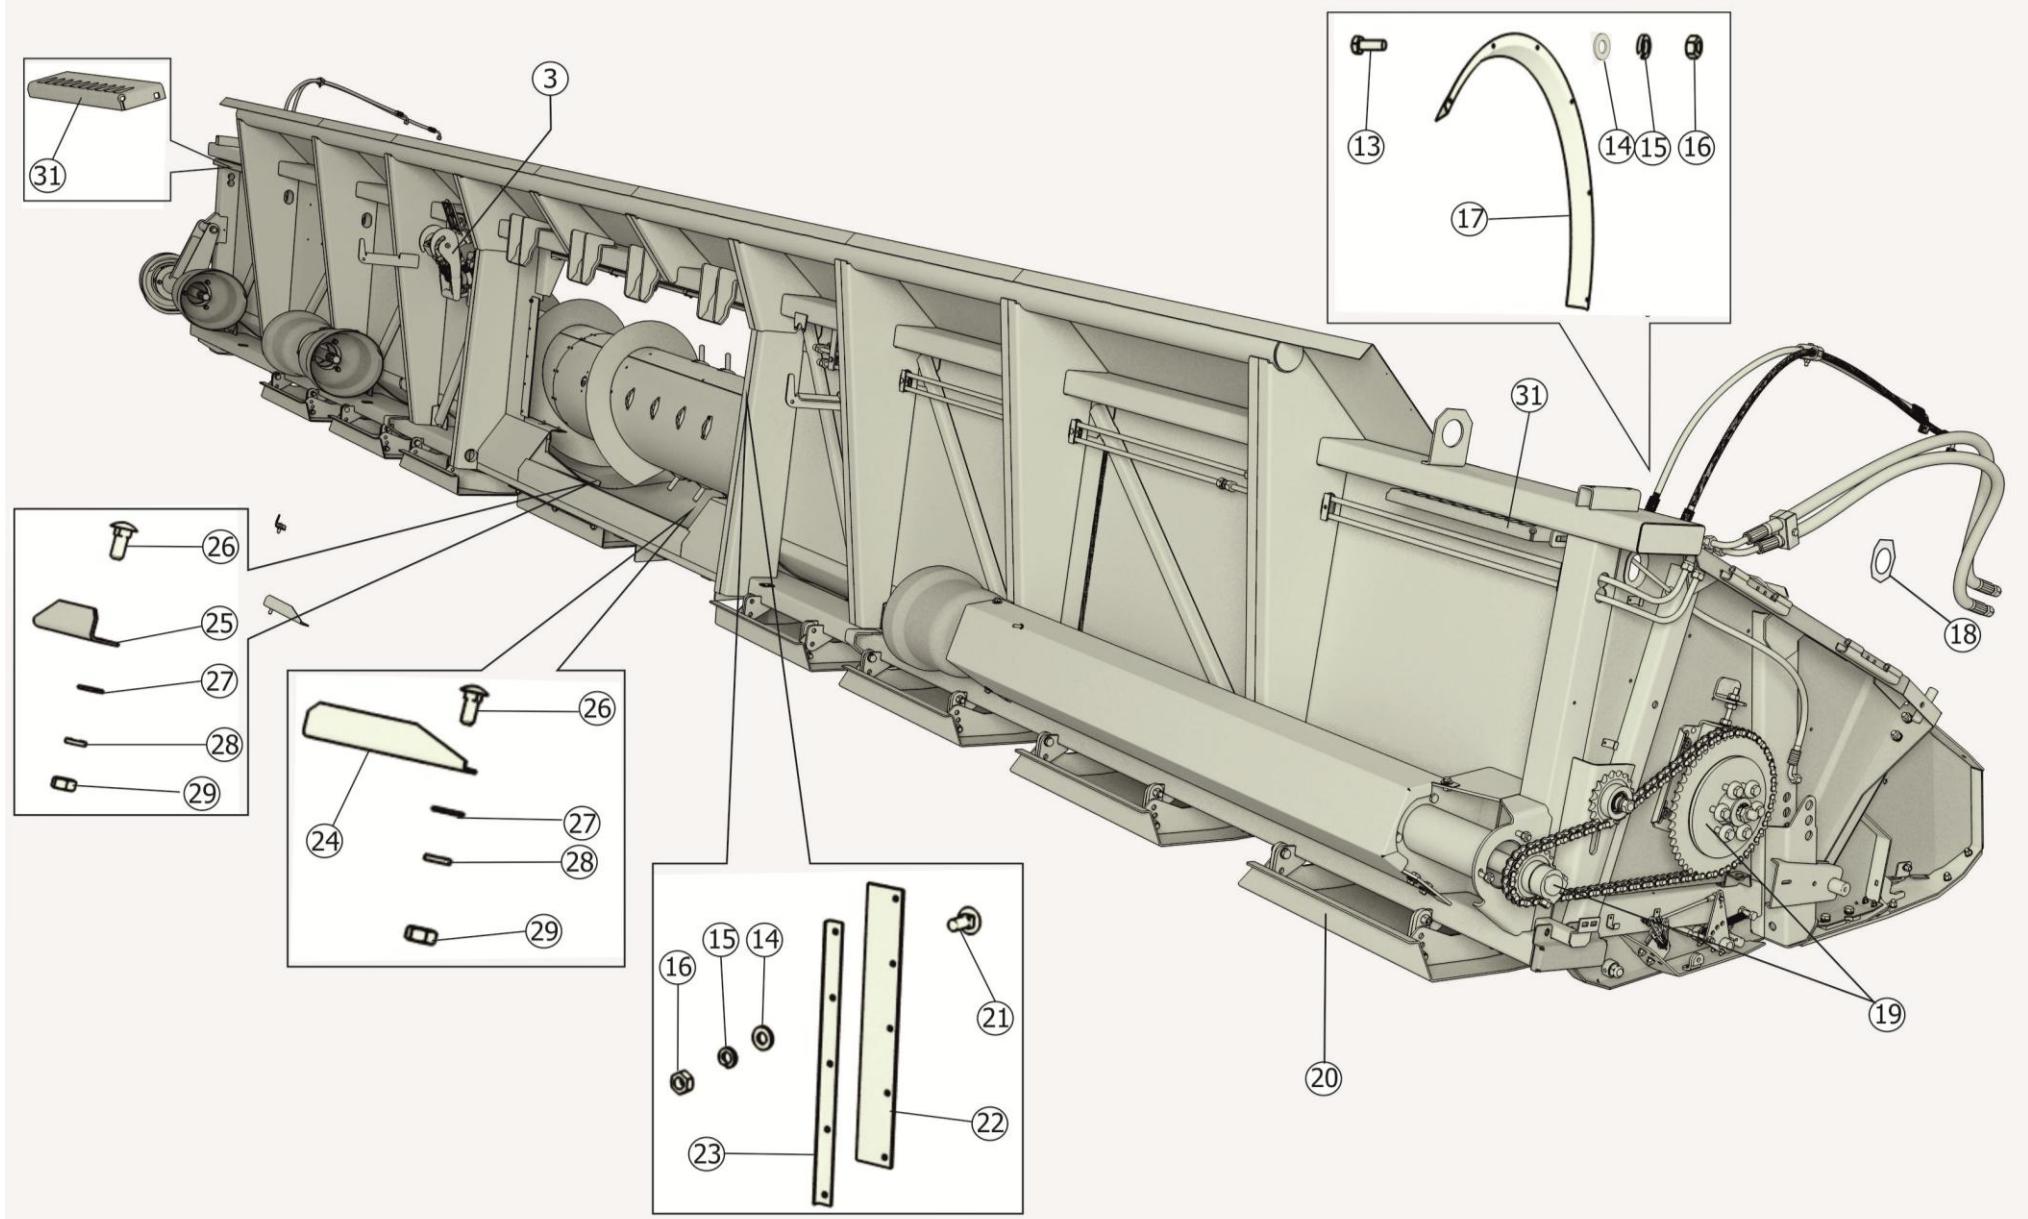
Корпус ЖСУ-901.01.00.000
